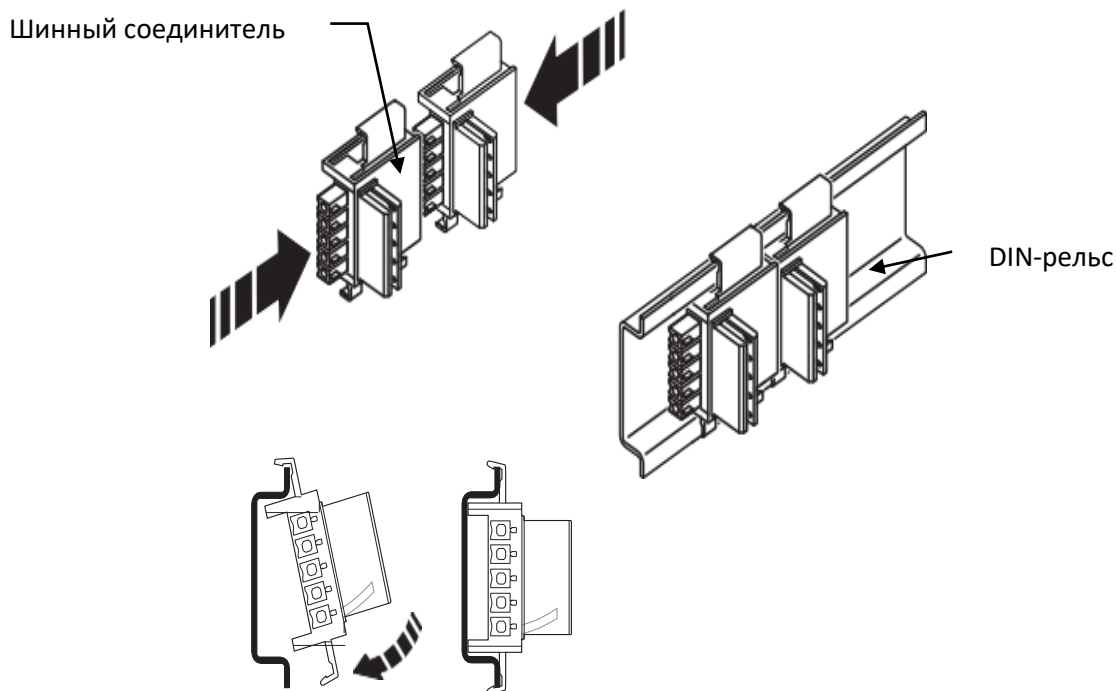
Схема установки шинных соединителей на DIN-рельс
